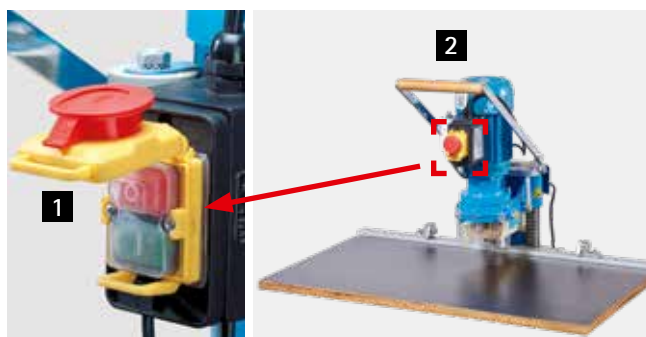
elementi di comando della macchina di foratura e montaggio a pressione
